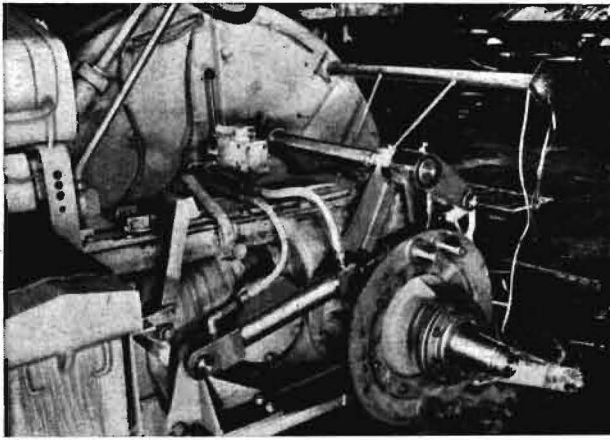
Anbau-Dreipunktaufhängung und -hydraulik am RS 01/40 „Pionier“ in Versuchsausführung
